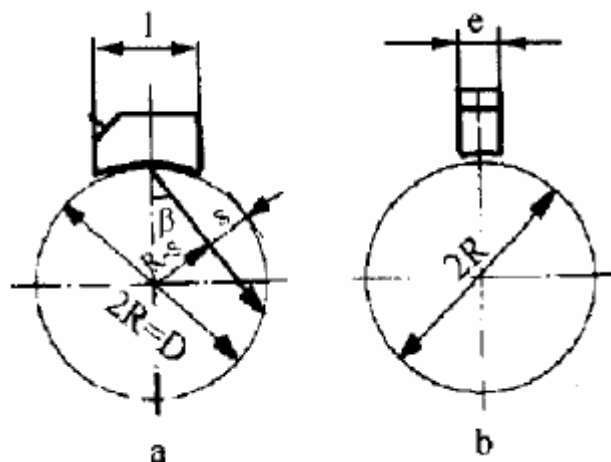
Adaptarea tălpii palpatorului la examinarea de pe suprafețe curbe: a) în plan transversal; b) în plan longitudinal
